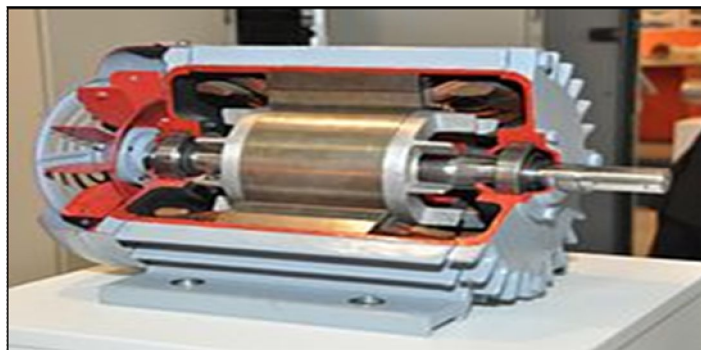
Rotor, estator y ventilador de un motor eléctrico
